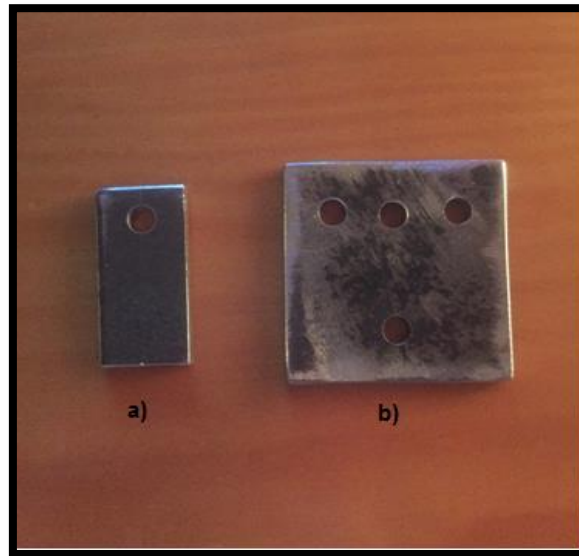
a) Chapa de 20x40 mm ; b) Chapa de 50x50mm
